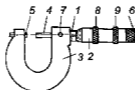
Устройство микрометра МК: 1 – стембель; 2 – барабан; 3 – скоба; 4 – измерительный стержень; 5 – пятка; 6 – трещотка; 7 – стопор измерительного стержня; 8 – накатное кольцо барабана; 9 – стопорная гайка барабана
